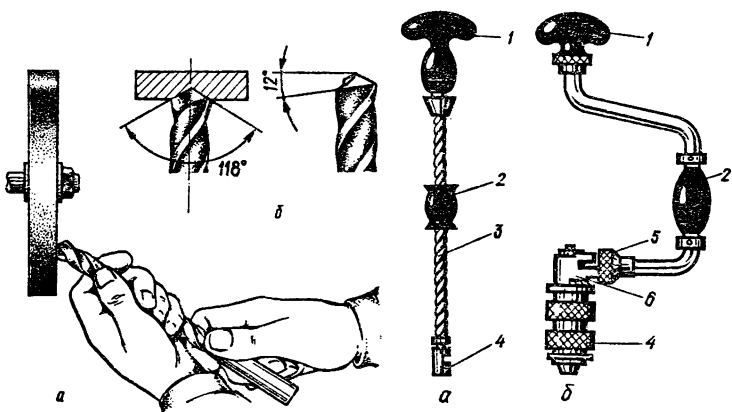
Ручная винтовая сверлилка (а) и коловорот (б): 1 — нажимная головка; 2 — ручка; 3 — стальной стержень с резьбой; 4 — зажимной патрон; 5 — кольцо-переключатель; 6 — храповой механизм.
